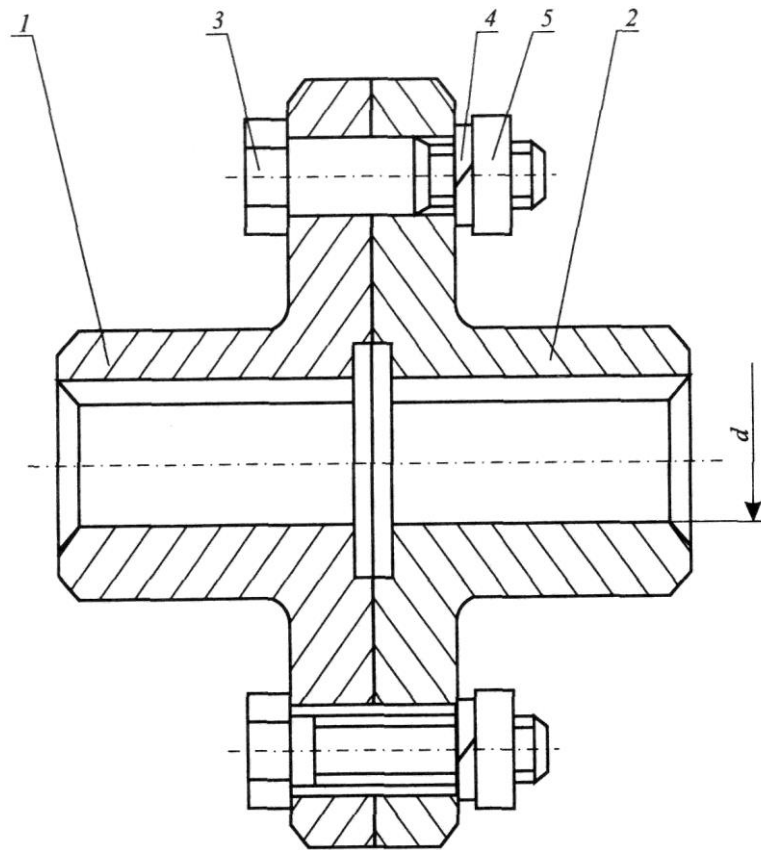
Муфта фланцева: 1 – півмуфта ліва; 2 – півмуфта права; 3 – болт; 4 – шайба пружинна; 5 – гайка.
